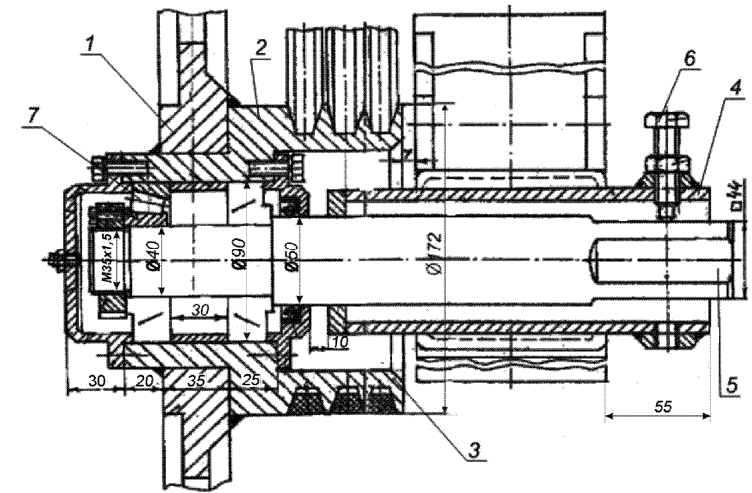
Вузол пилкового шківця механізму різання: 1) пилковий шків; 2) вал; 3) шків клинопасової передачі; 4) корпус; 5) вісь; 6) гвинт регулювання нахилу осі; 7) вальниця
